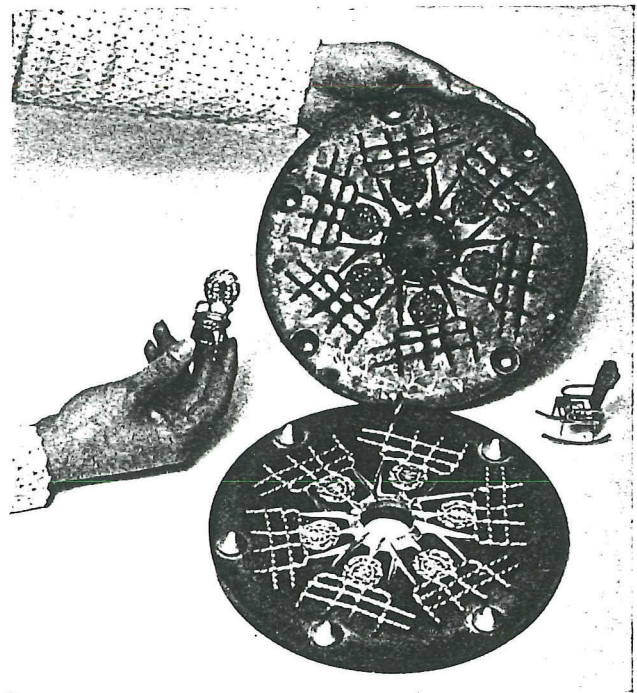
Fabrication d'objets décoratifs par coulée centrifuge dans des moules en caoutchouc.
